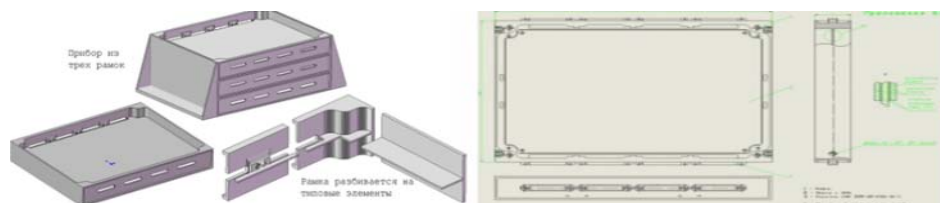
Внешний вид и чертеж унифицированной конструкции бортовой РЭА КА
